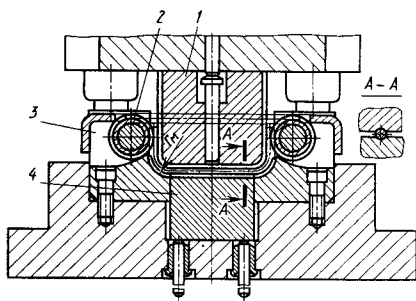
Штмп для U-образной гибки заготовки из прутка с применением роликов в матрице
